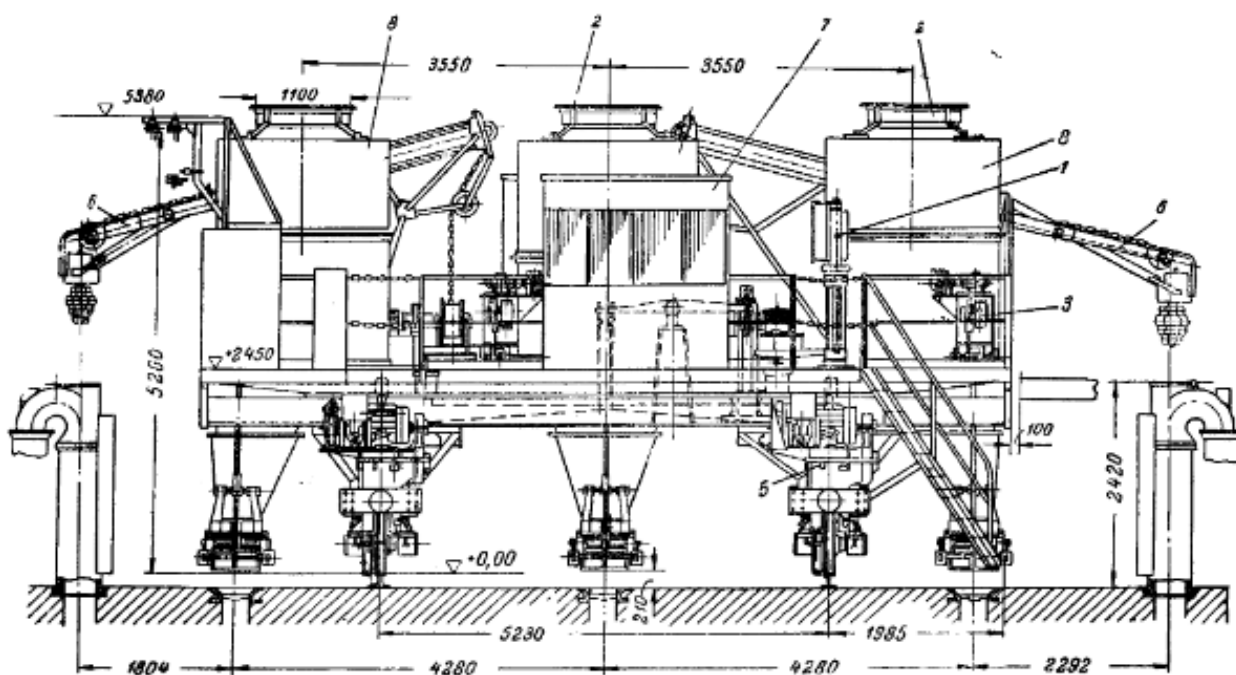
Трьохбункерний вуглезавантажувальний вагон конструкції конструкторського бюро Главмашмета. Вид спереду.
